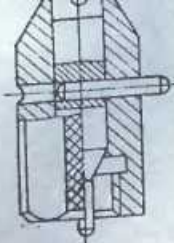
Приспособление ЛМ9571 - 006 для проверки подъема нагнетателя клапана
